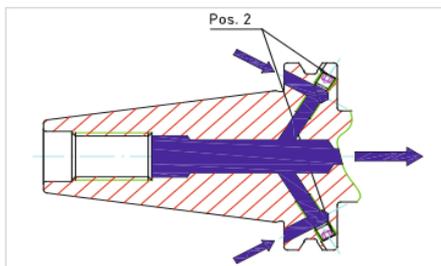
Kühlmittelzuführung Form AF/JF
